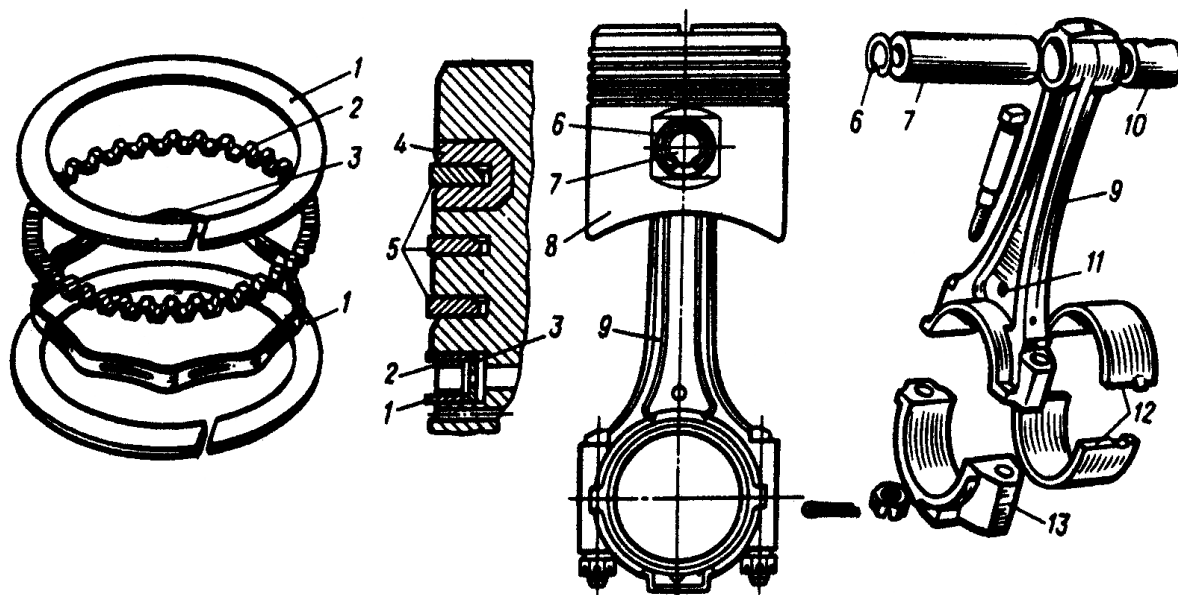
Детали шатунно-поршневой группы двигателя ЗиЛ-431410: 1 – маслосъемные кольца, 2 и 3 – осевой и радиальный расширители, 4 - чугунная вставка, 5 – компрессионные кольца, 6 – стопорное кольцо, 7 – поршневой палец, 8 – поршень, 9 – шатун, 10 – втулка, 11 – метка, 12 – шатунные вкладыши, 13 – крышка нижней головки шатуна
